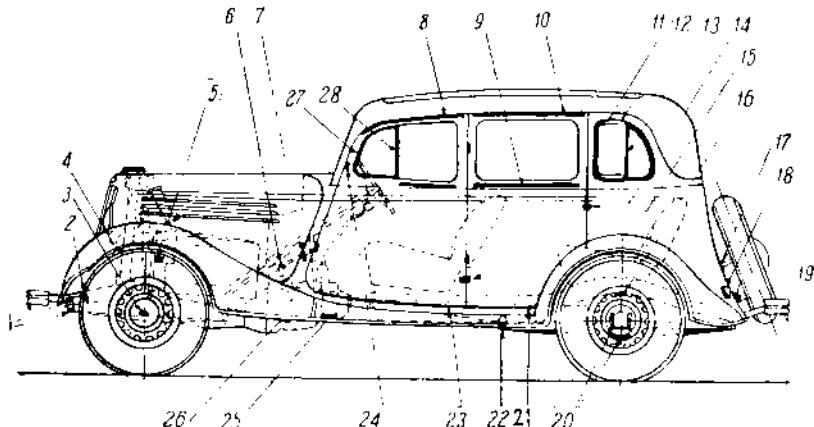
Схематическое расположение основных резиновых деталей в автомобиле М-1.
